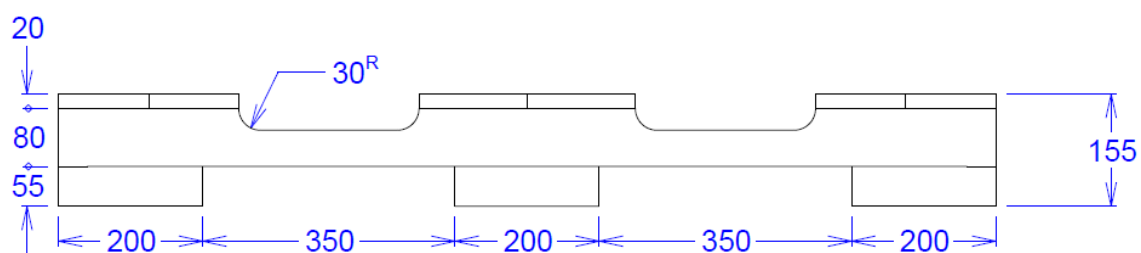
Desenho técnico proposto da paleta 1300x1300.
